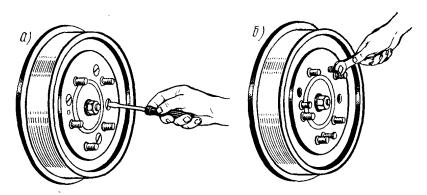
Снятие тормозного барабана со ступицы колеса: a — отвертывание винтов крепящих барабан к ступице; δ — снятие барабана завертыванием болтов в отверстия
